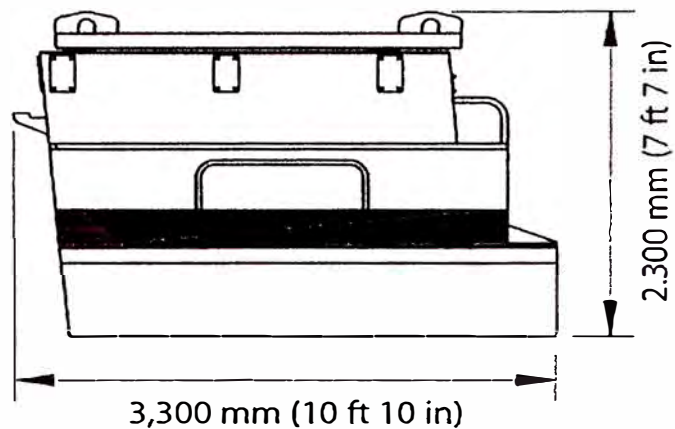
Dimensiones del Módulo Pedestal de Cabina
